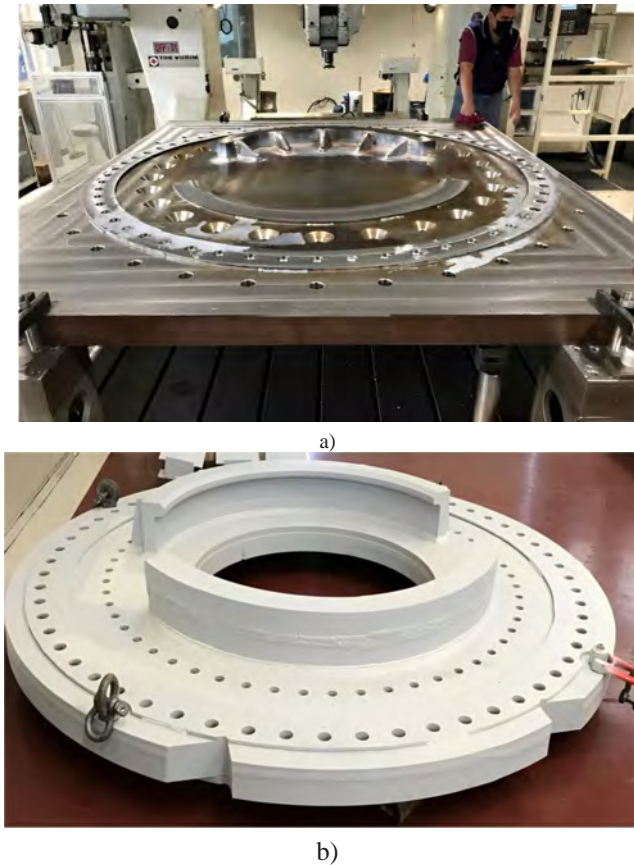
a) Maquinado de placa base, b) placa adaptadora terminada
